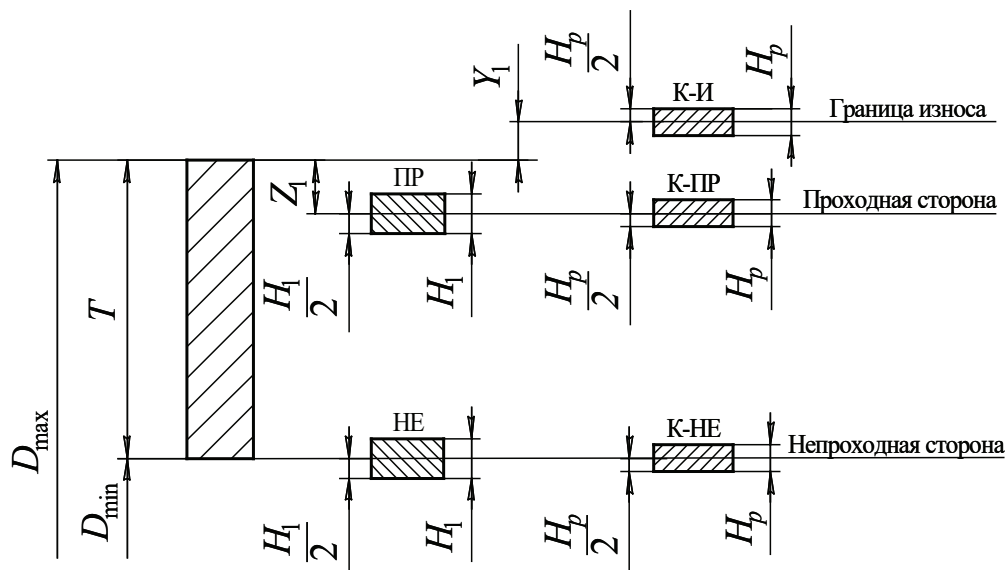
Схема расположения полей допусков для калибров-скоб
